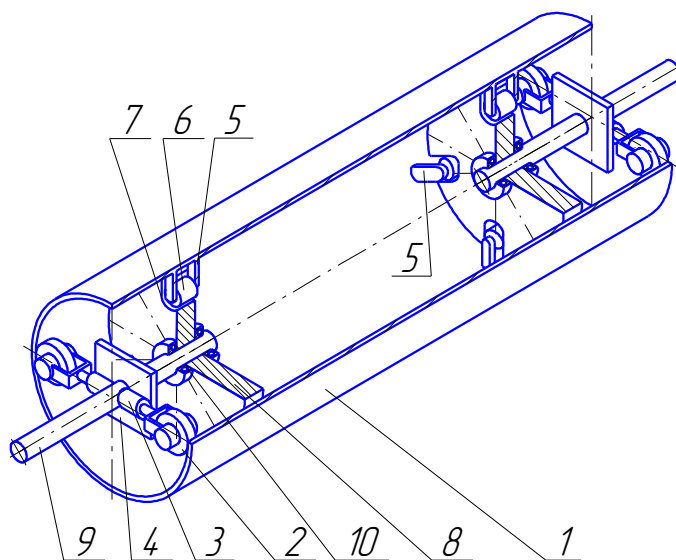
Схема вальца с гибкой обечайкой по патенту РК № 18131. А.с. на изобретение РК № 51084: 1– обечайка; 2-упорные ролики; 3– гидроцилиндры
